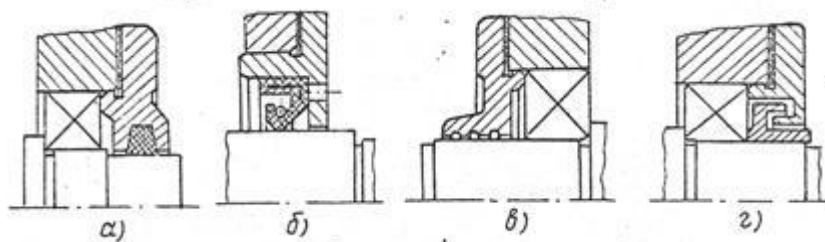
Уплотнительные устройства подшипниковых узлов
